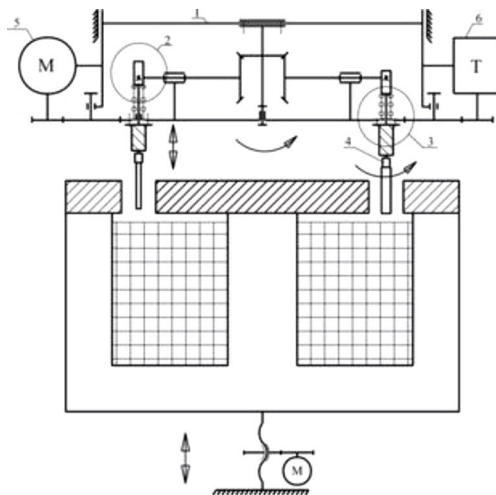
Кинематическая схема установки для МАП компрессорных лопаток:
